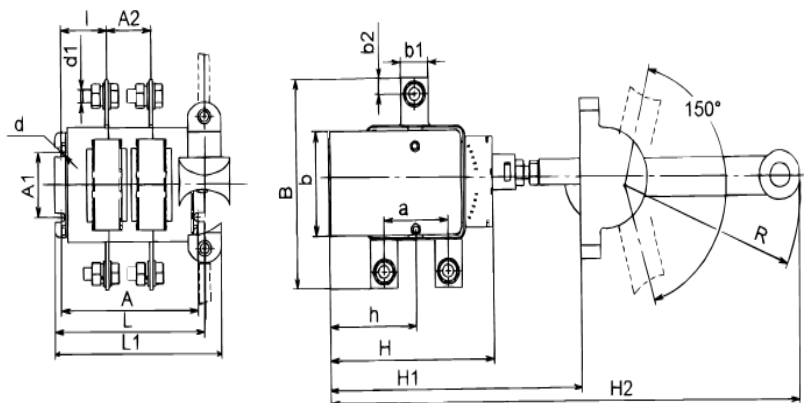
Б Выключатель-разъединитель на два направления двухполюсный с передней смещенной рукояткой
